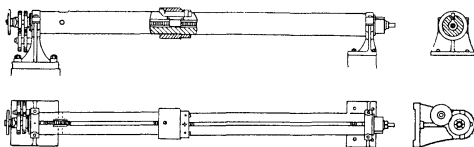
Борштанга станка Вилкинсона. 1775 г. Чертеж с натуры.
